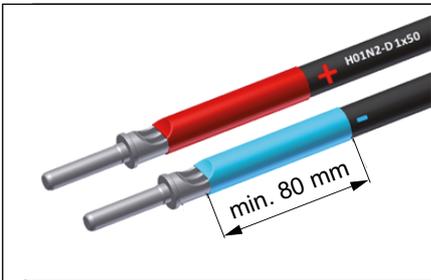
Lage und Maße für den Schrumpfschlauch von 16 mm² bis AWG 4/0 mittig zur Crimpung; Schrumpfschlauchlänge mind. 80mm
